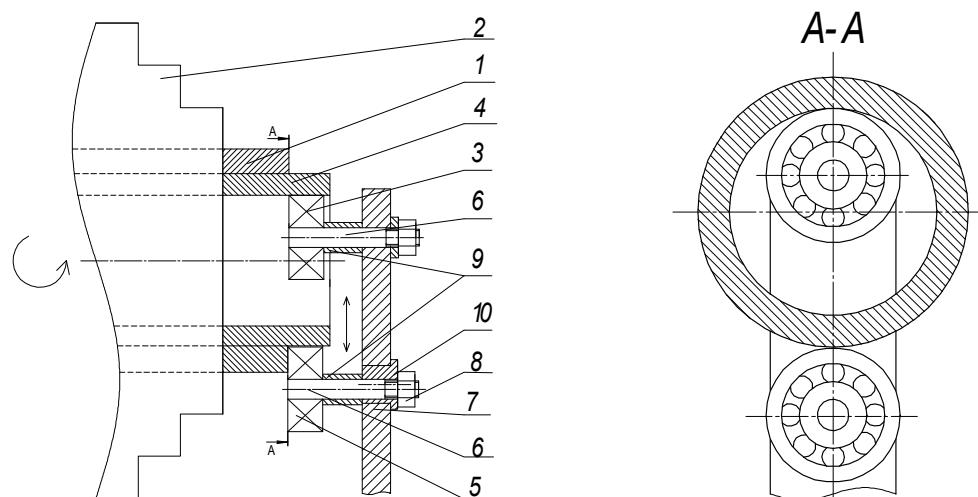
Устройство для отрезки трубчатых заготовок от цилиндрической трубы
